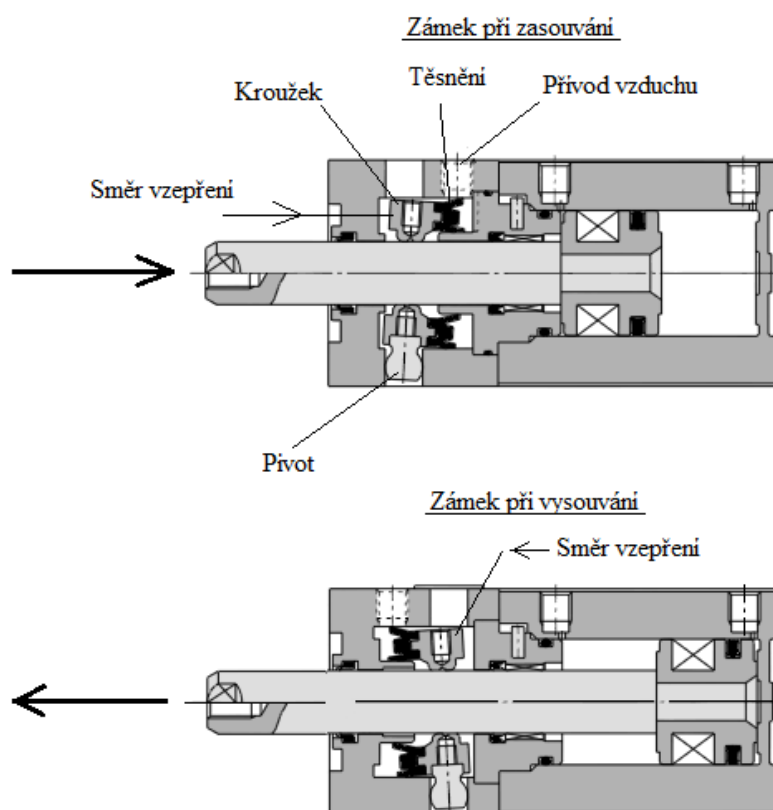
Konstrukce pasivní brzd Multi-brake
